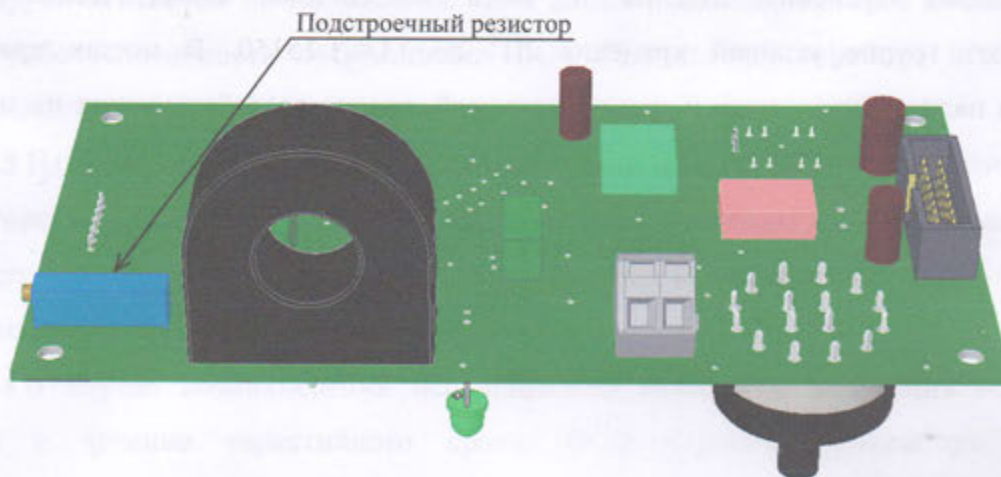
Печатная плата и расположение подстроечных резисторов (вид со стороны пайки)
